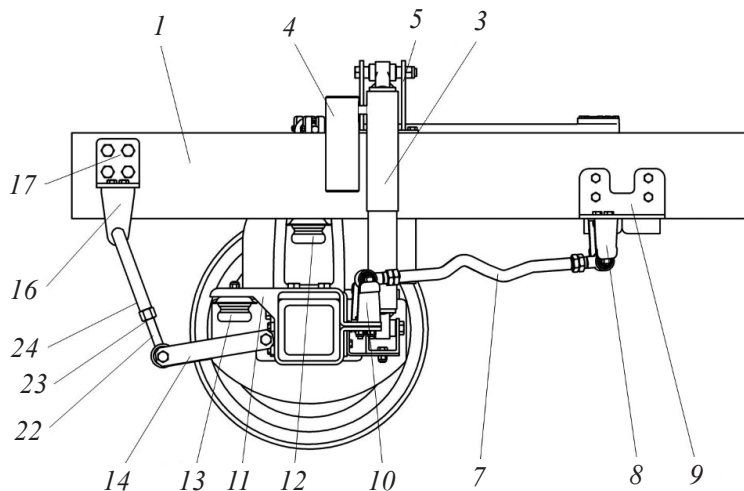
Задняя подвеска транспортного средства, вид сбоку: 1 – рама; 3 – амортизатор; 4 – внешняя пневмокамера; 5 – верхний кронштейн амортизатора; 7 – нижняя штанга; 8, 16 – стойки; 9, 10, 17 – кронштейны; 11 – накладка; 12 – буфер сжатия; 13 – буфер отбоя; 14 – серьга; 22 – резьбовой стержень; 23 – контргайка; 24 – трубчатый конец стабилизатора
